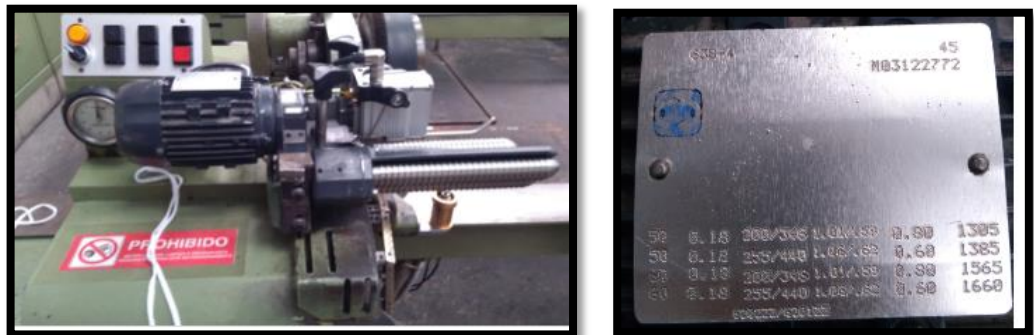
14. Motor desenrollador de orillos y dato de placa
